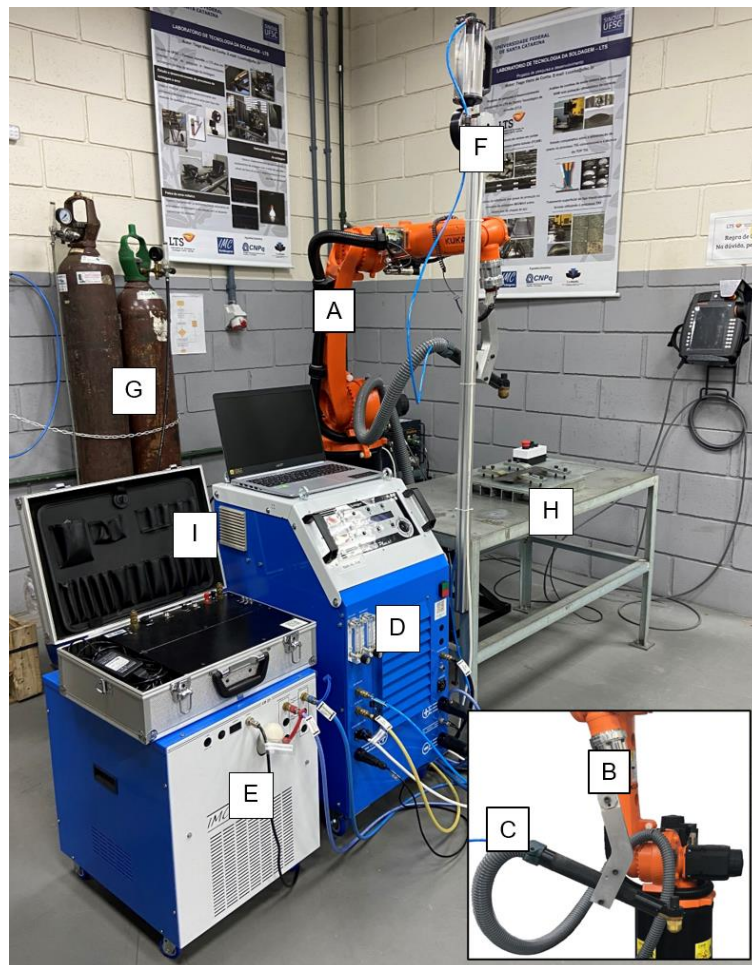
Bancada de ensaios composta por (A) robô de soldagem, (B) punho de fixação, (C) tocha de soldagem, (D) fonte de soldagem, (E) unidade de refrigeração, (F) alimentador de pó, (G) cilindros de gás e (H) dispositivo de fixação dos corpos de prova (I) sistema de aquisição SAP
